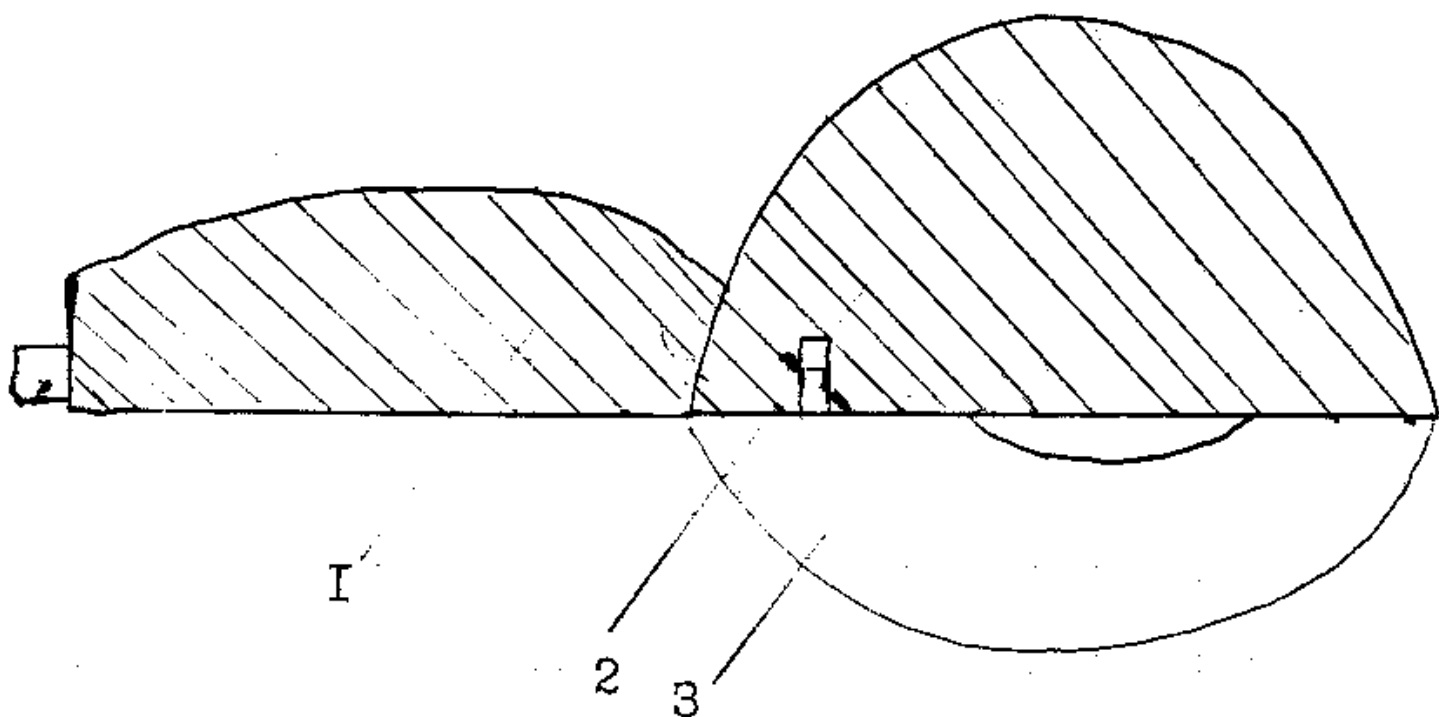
Светильник консольный Р/Ж/КУ 03-250-00Г: I --- корпус с находящимися внутри ПРА и ИЗУ, 2 -- отражатель 3 -- лампа типа ДРЛ 250, или ДНаТ 250.
